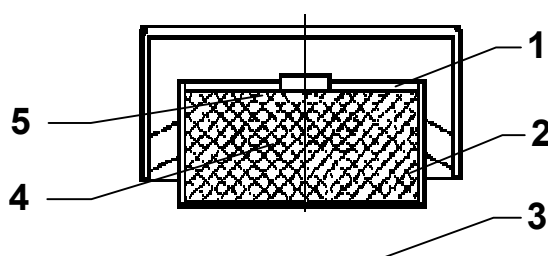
Конструкция генератора с коаксиально расположенными полукорпусами: 1 – внешний полукорпус; 2 – внутренний полукорпус; 3 – аэрозолеобразующий заряд; 4 – воспламенитель; 5 – слой охладителя
